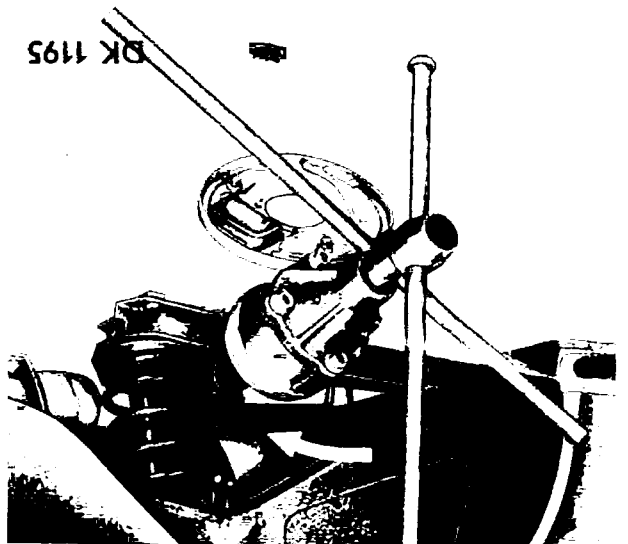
/7 Abdrücken der Welle vom Lager mit Hilfe der Montagevorrichtungen MP 5-111 und MP 5-113
